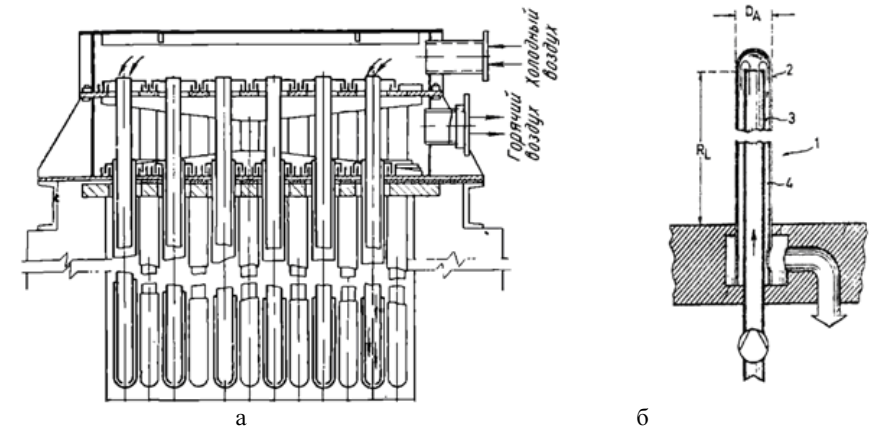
Трубчатый рекуператор двойной циркуляции (а) [8], рекуператор Didieder-Werke AG (Вайсбаден) (б) [28]: 1) рекуператор; 2) наружная труба; 3) внутренняя труба; 4) осевой зазор; 5) отводящий патрубок
